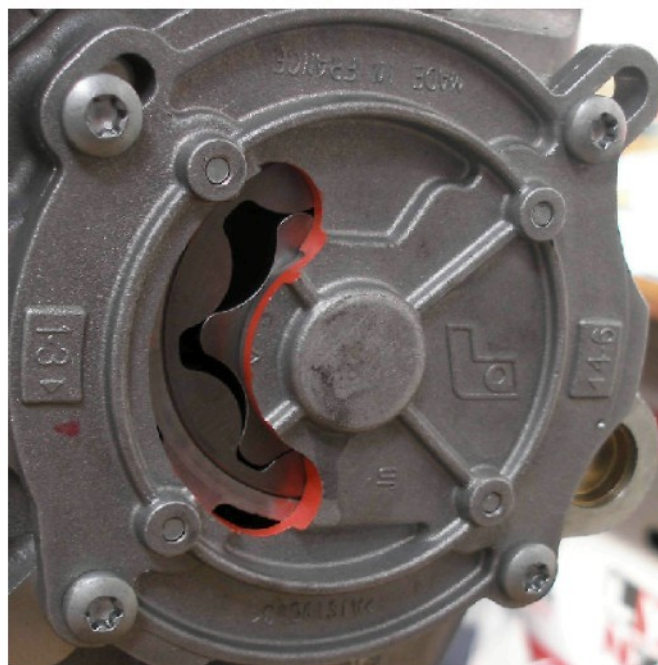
Řez bokem motoru | foto dokumentace autora |
